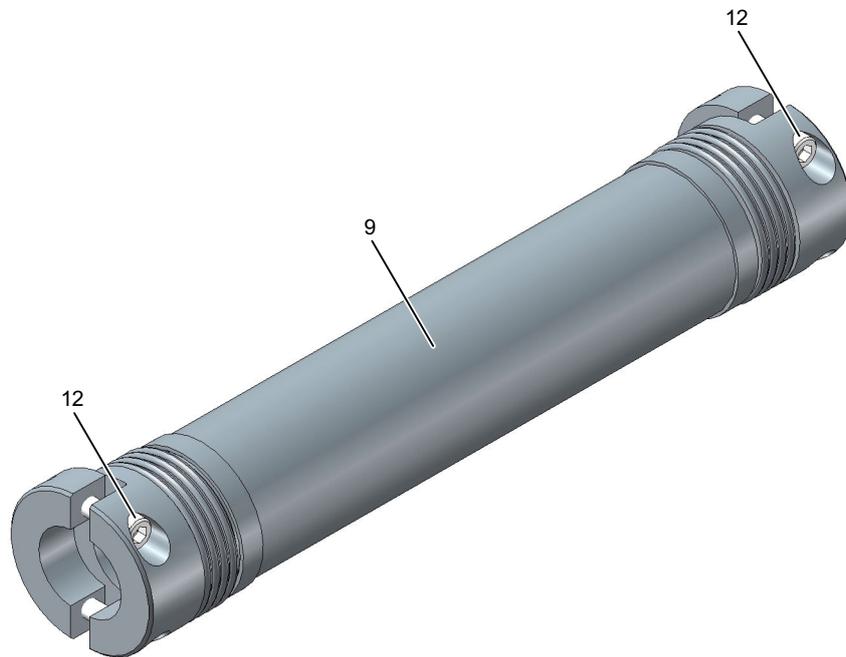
Ersatzteilzeichnung für Bauart SHH-W
